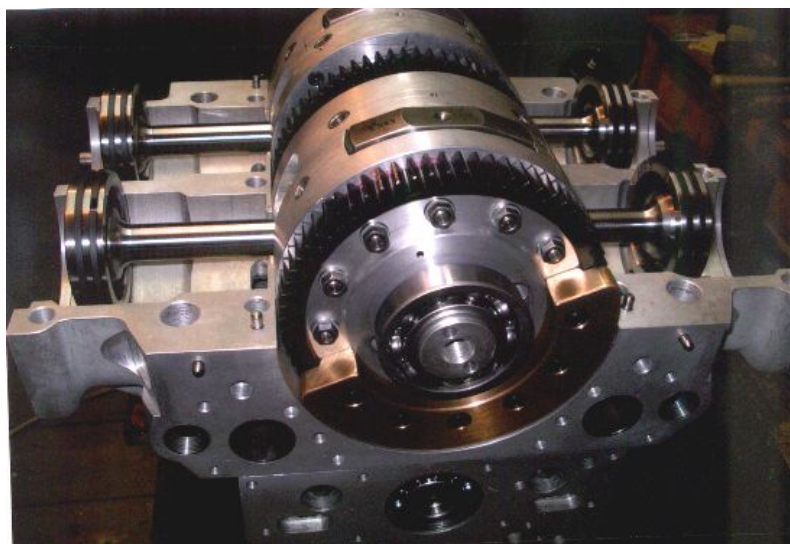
Общий вид четырехцилиндрового двигателя по схеме С.С.Баландина, разработанного А. Вулем
